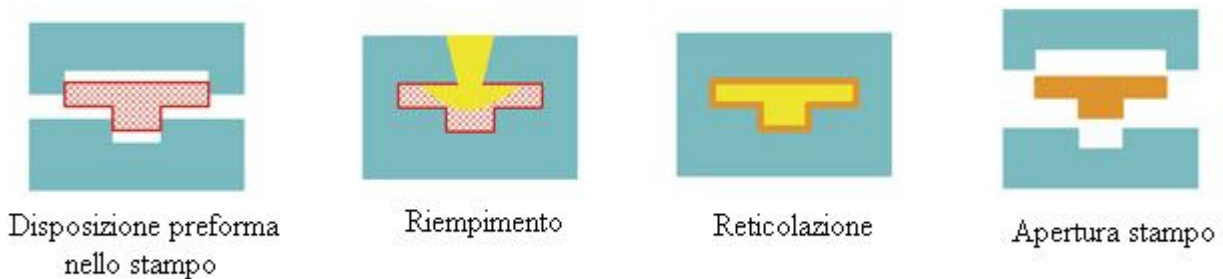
fasi del processo di stampaggio R.T.M.
